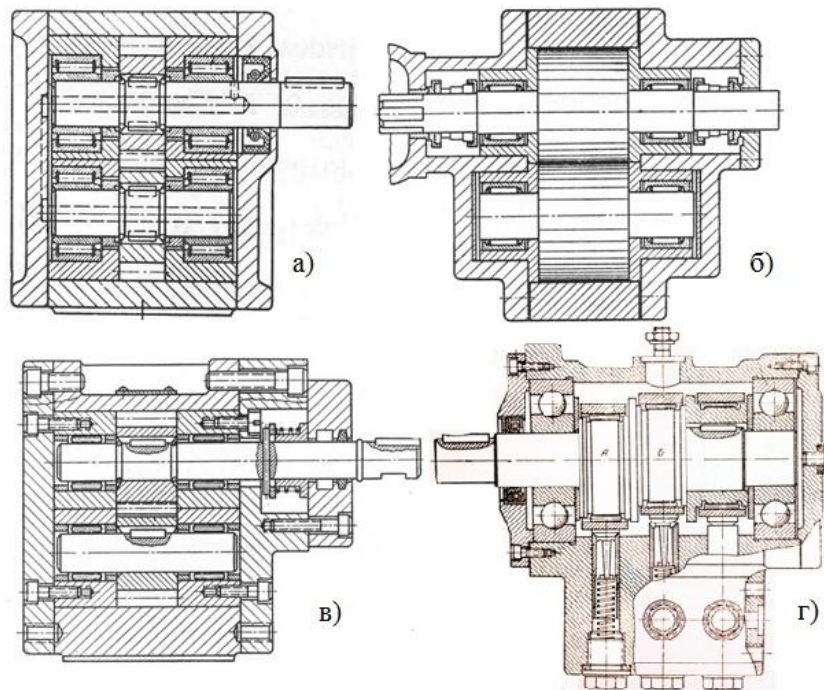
Конструкции насосов с игольчатыми подшипниками опор: а) шестеренного насоса Г11-2 с двумя кольцами (обоймами) подшипника; б) подшипник с одним наружным кольцом и внутренней дорожкой качения на валу (шипе) шестерни; в) подшипник без колец с дорожками качения на валу и втулках (торцевых замыкателях); г) конструкция радиально-плунжерного эксцентрикового насоса типа Н400
